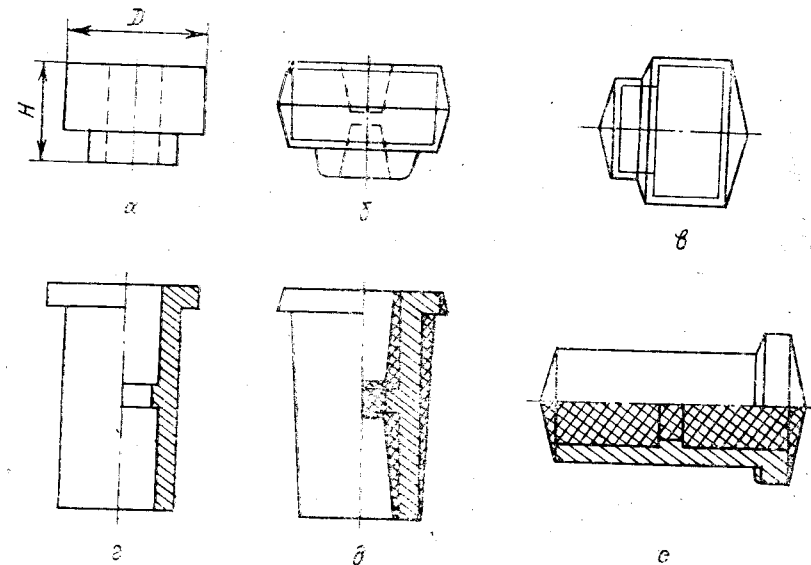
Залежність форми кованки від розташування площини рознімання штампів:
